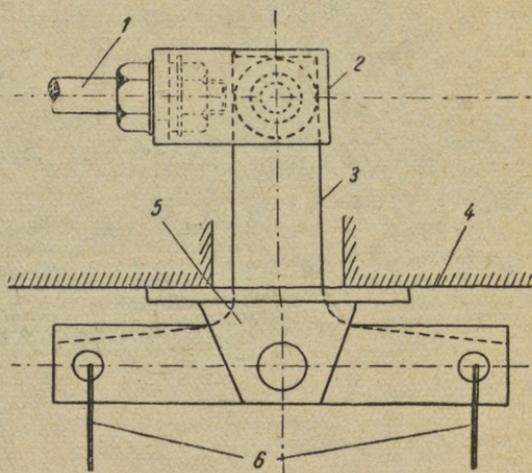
Неправильно изготовленный верхний трехплечий рычаг:
